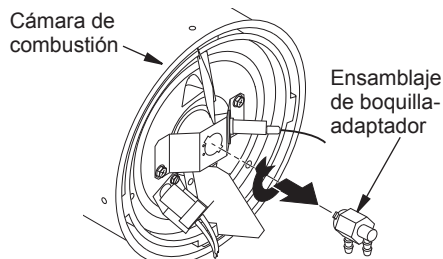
Desmontaje del ensamblaje de la boquilla-adaptador
